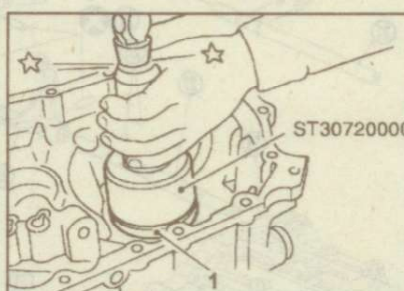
Использование оправки для установки наружного кольца подшипника (1) дифференциала
